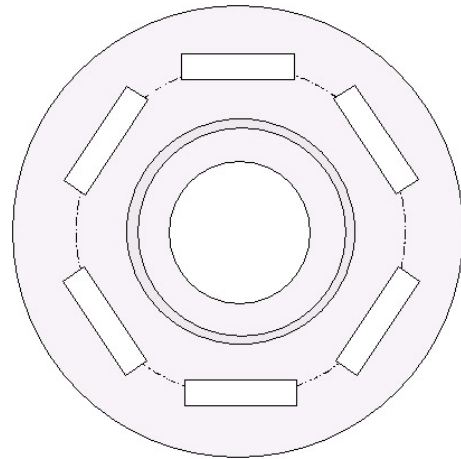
Prélèvement des éprouvettes sur un disque de frein
